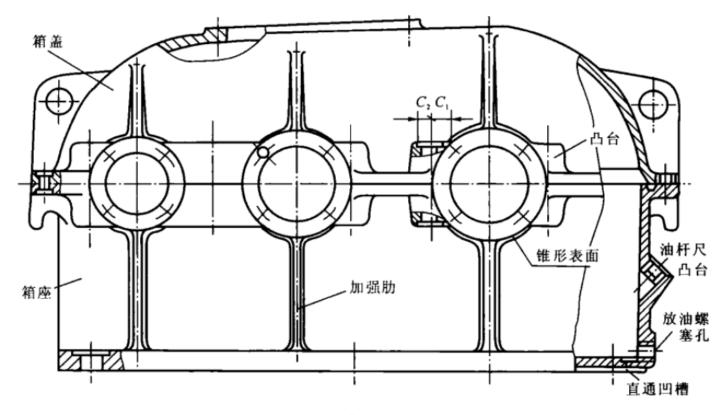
两级圆柱齿轮减速器箱体(剖分式)
